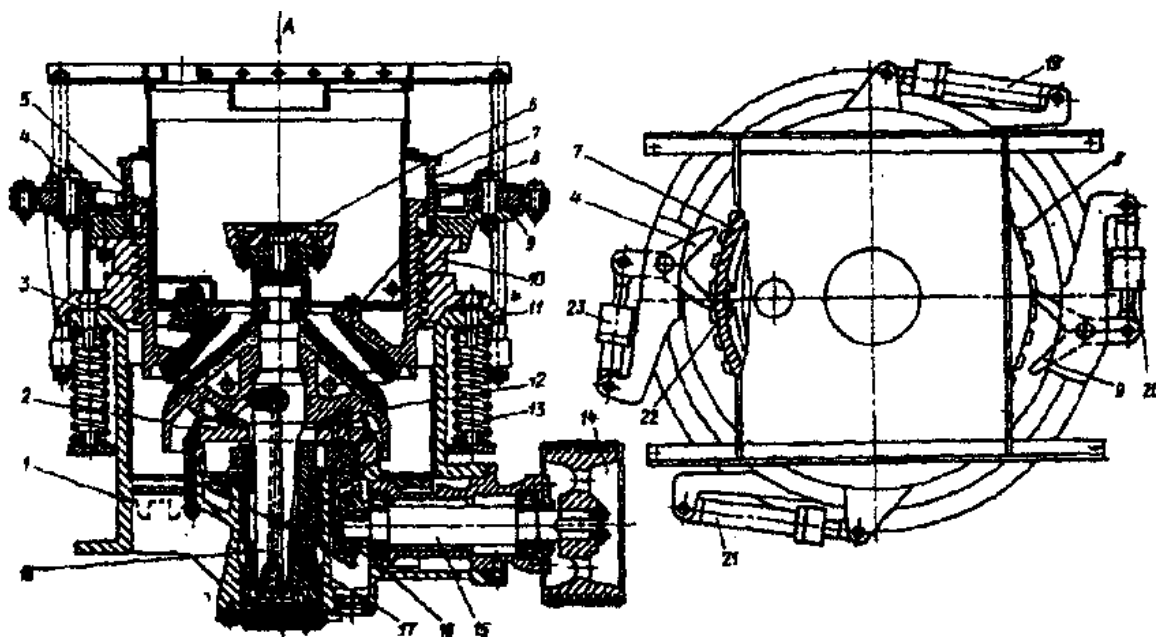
Конусна дробарка з гідравлічним пристроєм для регулювання ширини вихідної щілини
